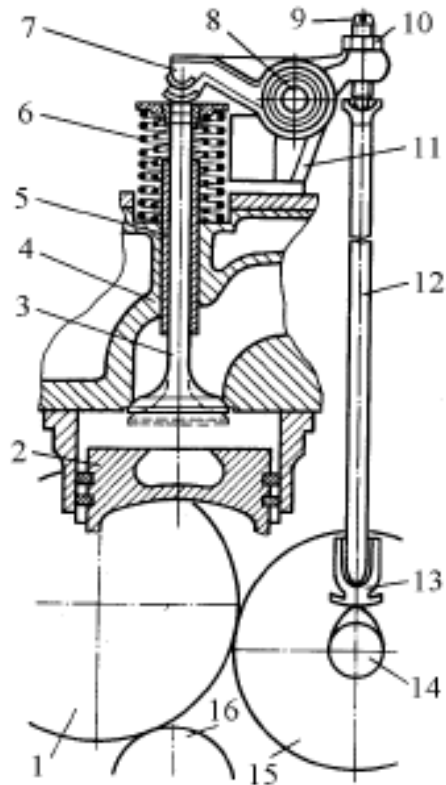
Схема распределительного механизма с верхним расположением клапана и нижним распредвала:
